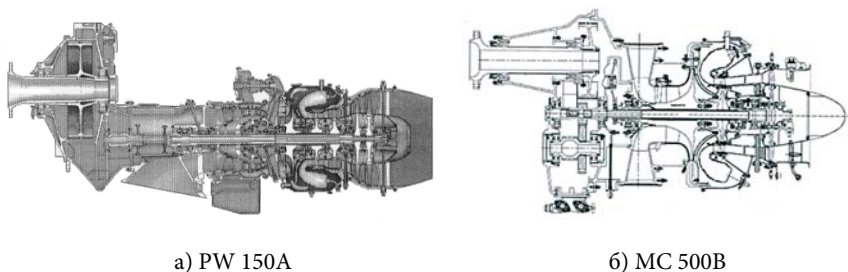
Схемы двигателей с редуктором, включенным в конструкцию двигателя, приводимым от ротора свободной турбины и расположенным спереди
